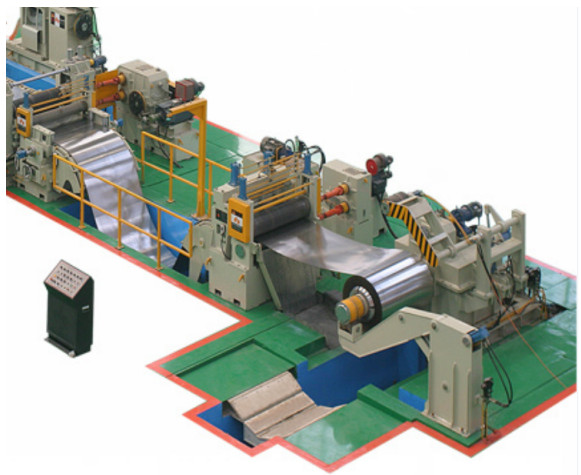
Maquinaria china. Taizhou Hitech NC Machine Tool Co., Ltd.
